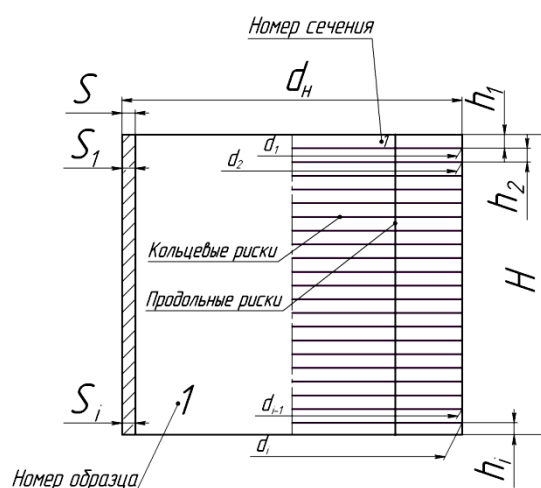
Эскиз исходной трубной заготовки с нанесёнными рисками
